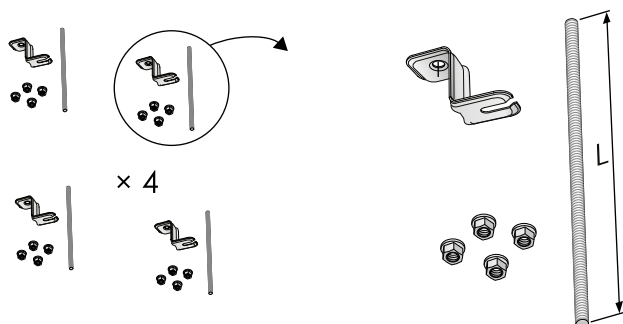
Élément d'assemblage SYST MS M8-1, montage au plafond et sur tige filetée
